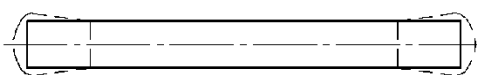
Уширение при прокатке полосовой заготовки переменной толщины
